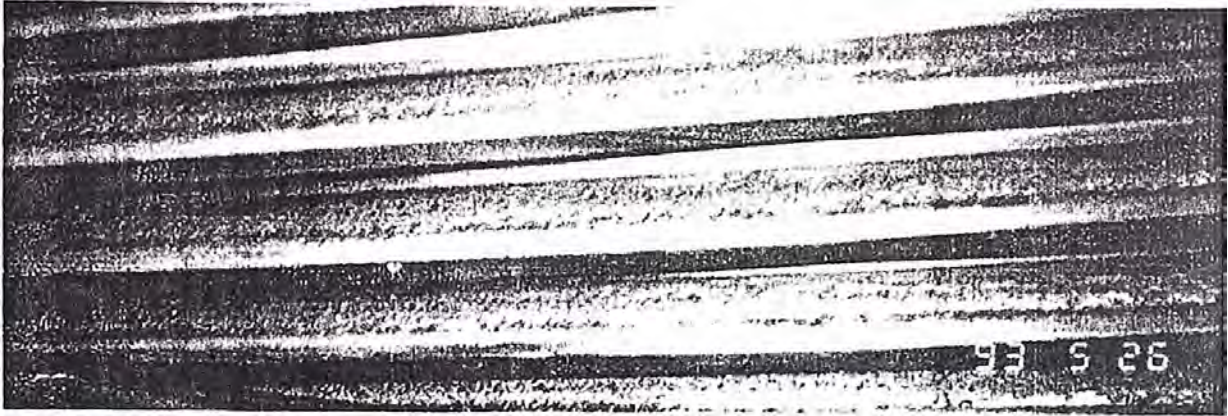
Picadura presentada en el engranaje de reductor Molino de Crudo II (apariencia de picadura severa)
